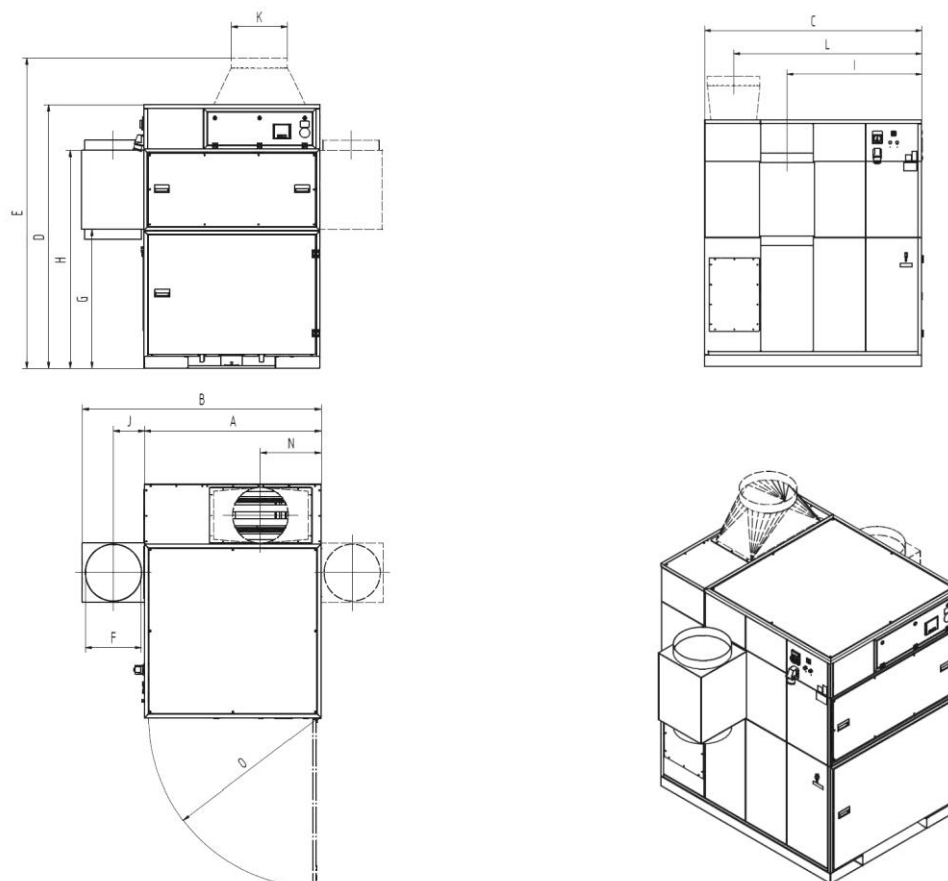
Габаритный чертеж 3550, 3565, 3750, 325019
